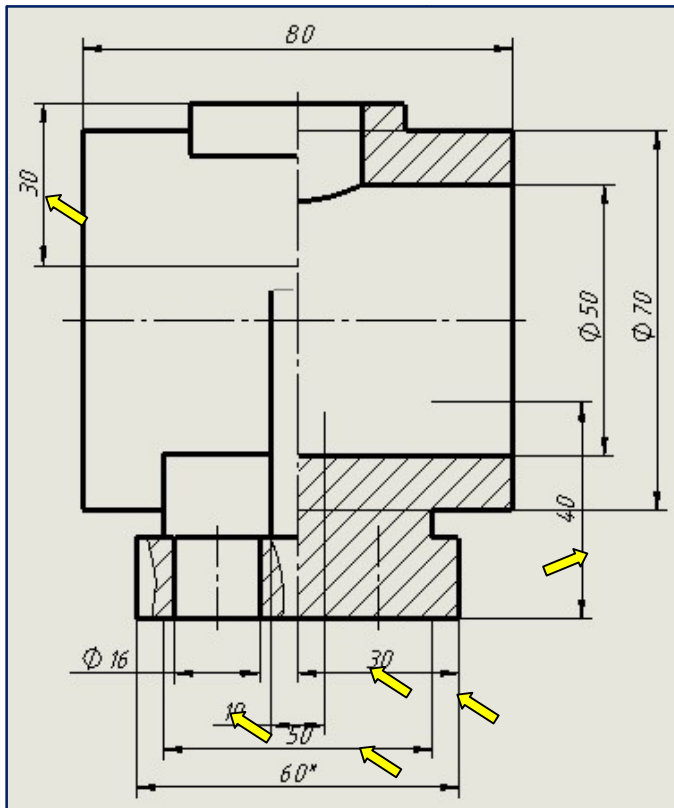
73. Размеры Чертёжного вида 2 импортированные из модели
